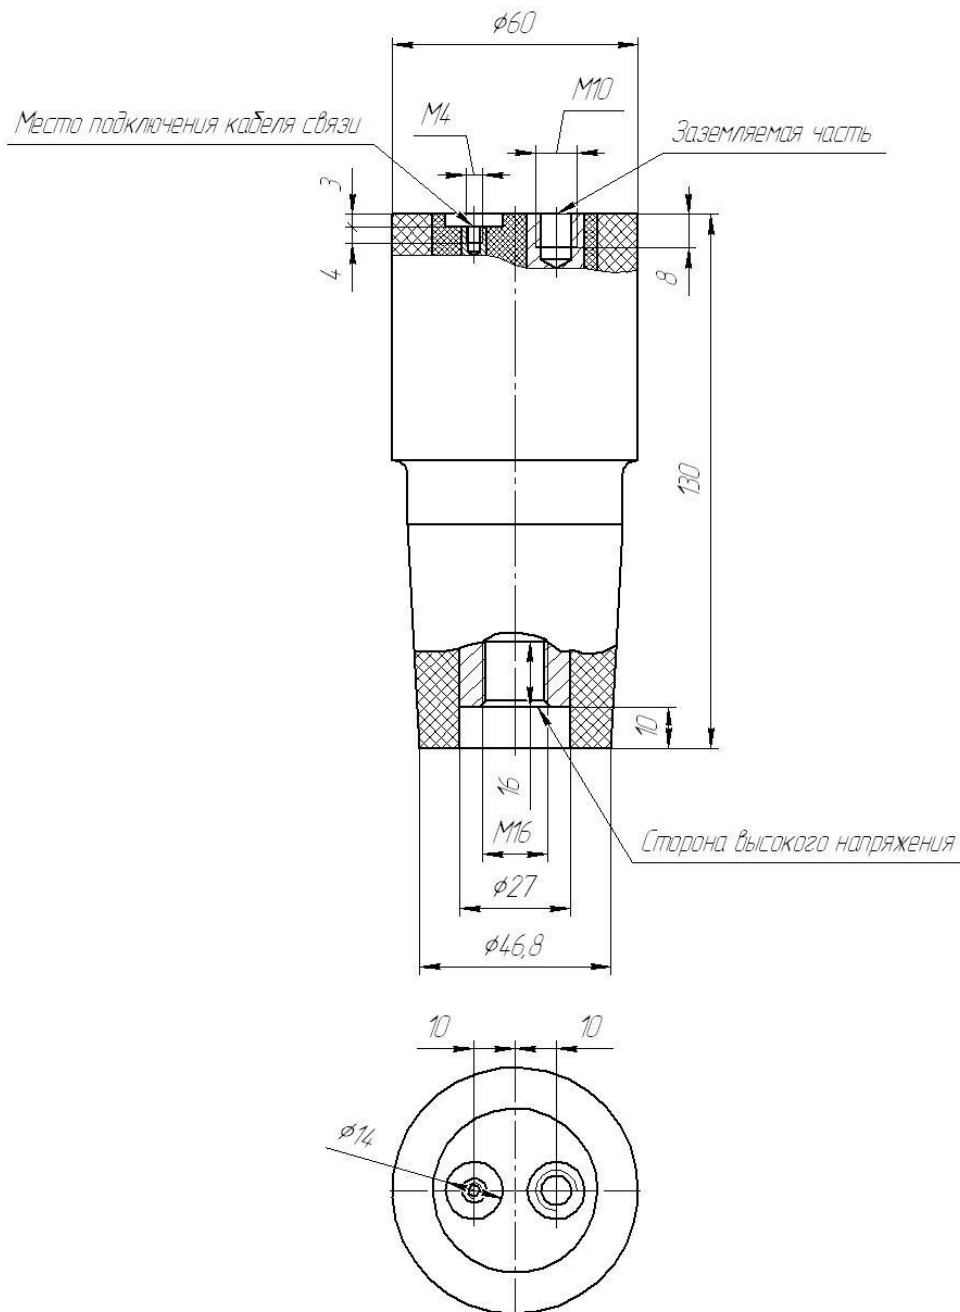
Габаритные, установочные и присоединительные размеры измерительного компонента устройства I-TOR-6(10)-U, конструктивное исполнение - навинчиваемое.
